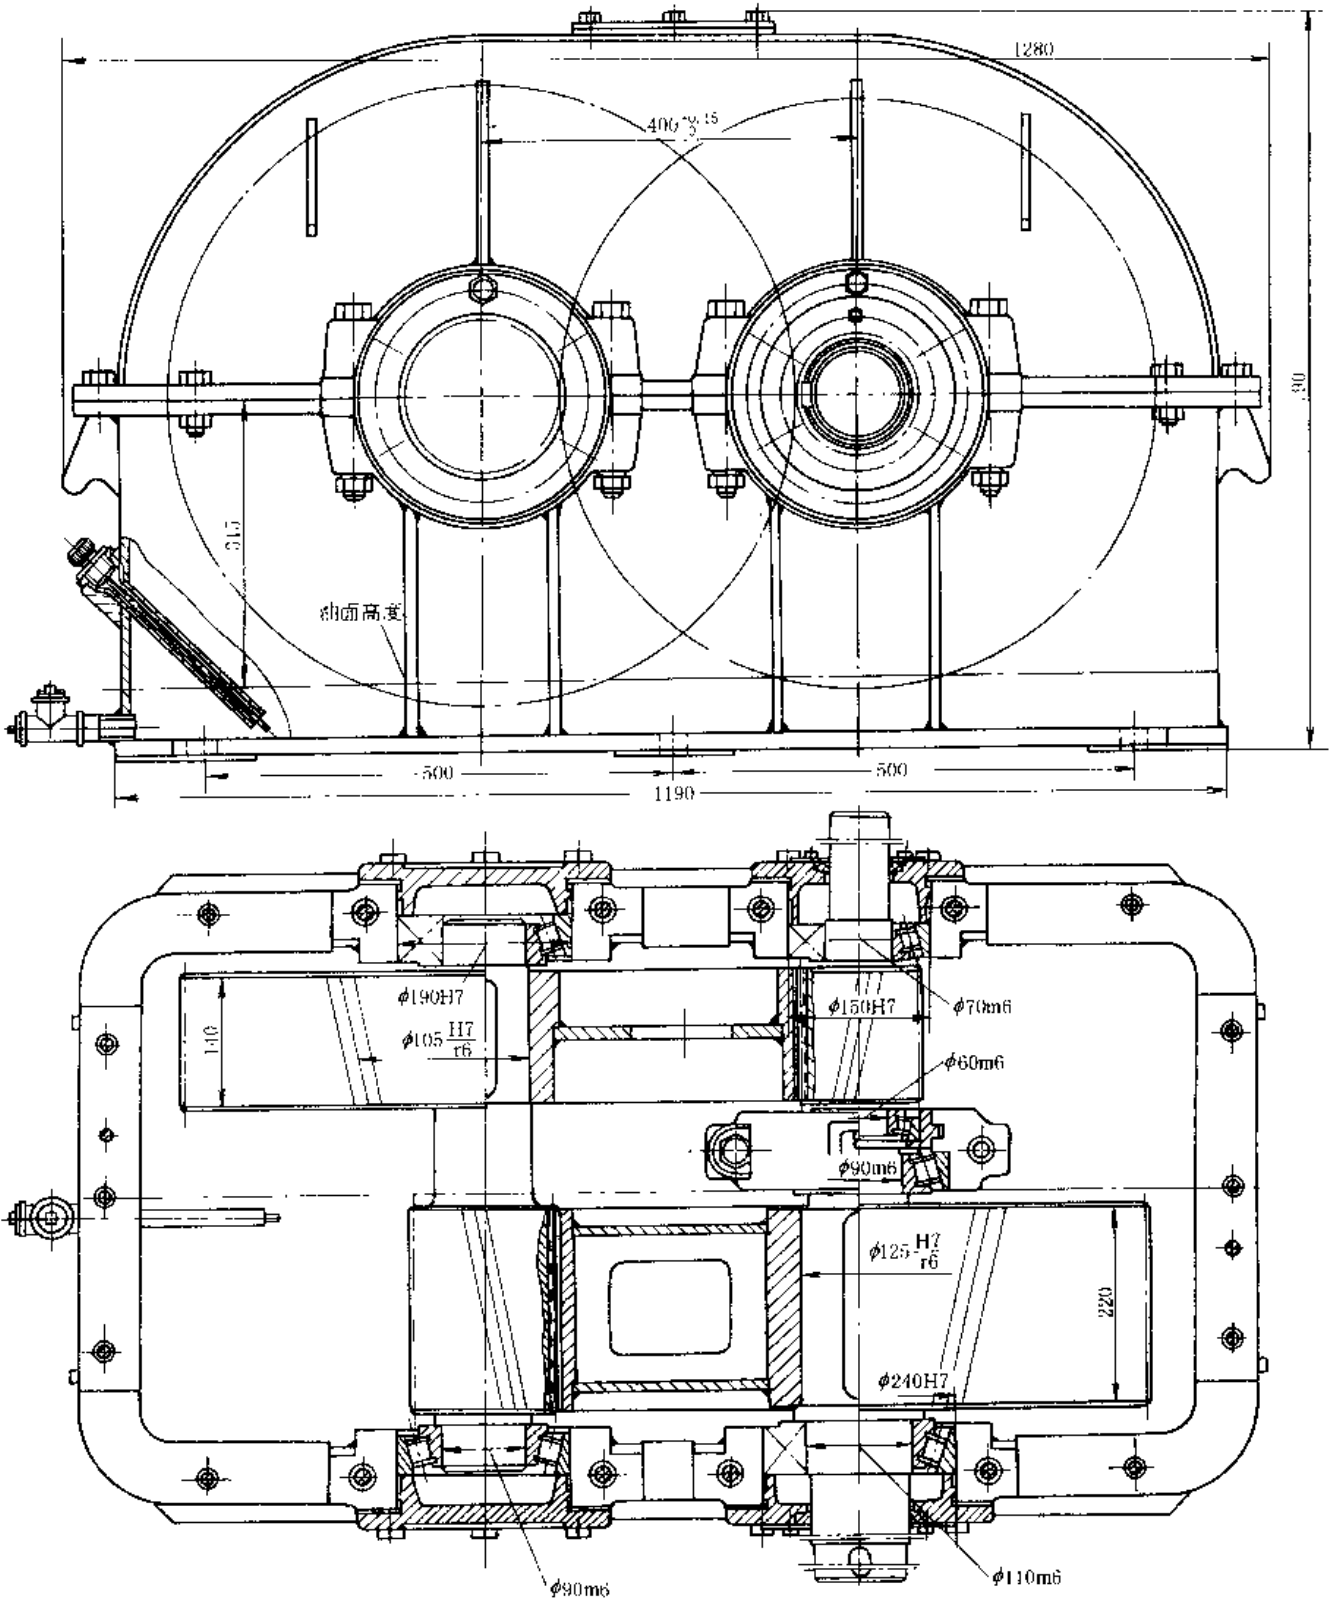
两级同轴线式圆柱齿轮减速器（焊接箱体和大齿轮）
